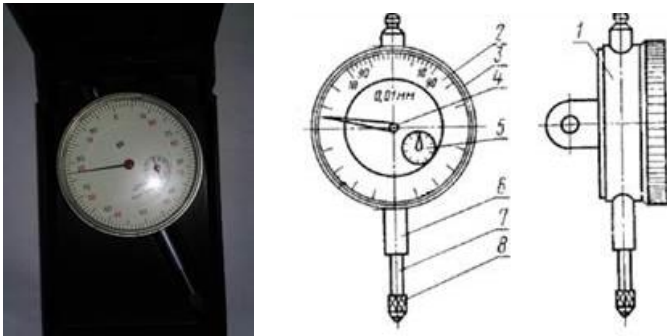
Загальний вигляд індикатора годинникового типу:
